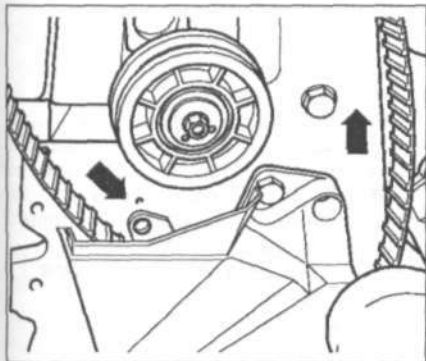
Прокрутите шкив промежуточного вала с зубчатым ремнем в направлении движения настолько, чтобы рычаг ротора совместился с меткой для цилиндра №1 на корпусе распределителя (над шкивом коленчатого вала).
